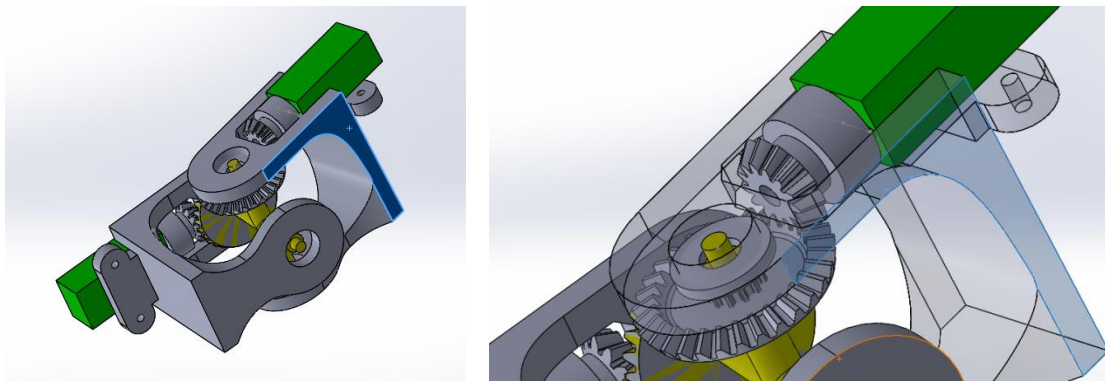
28 Diseño del ensamblaje de la muñeca con engranajes conicos
